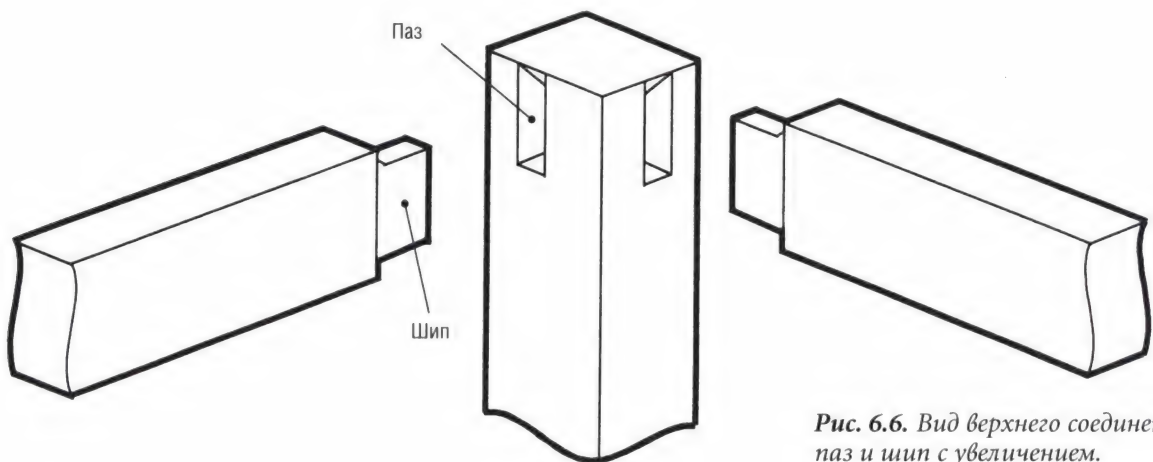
Вид верхнего соединения паз и шип с увеличением.
